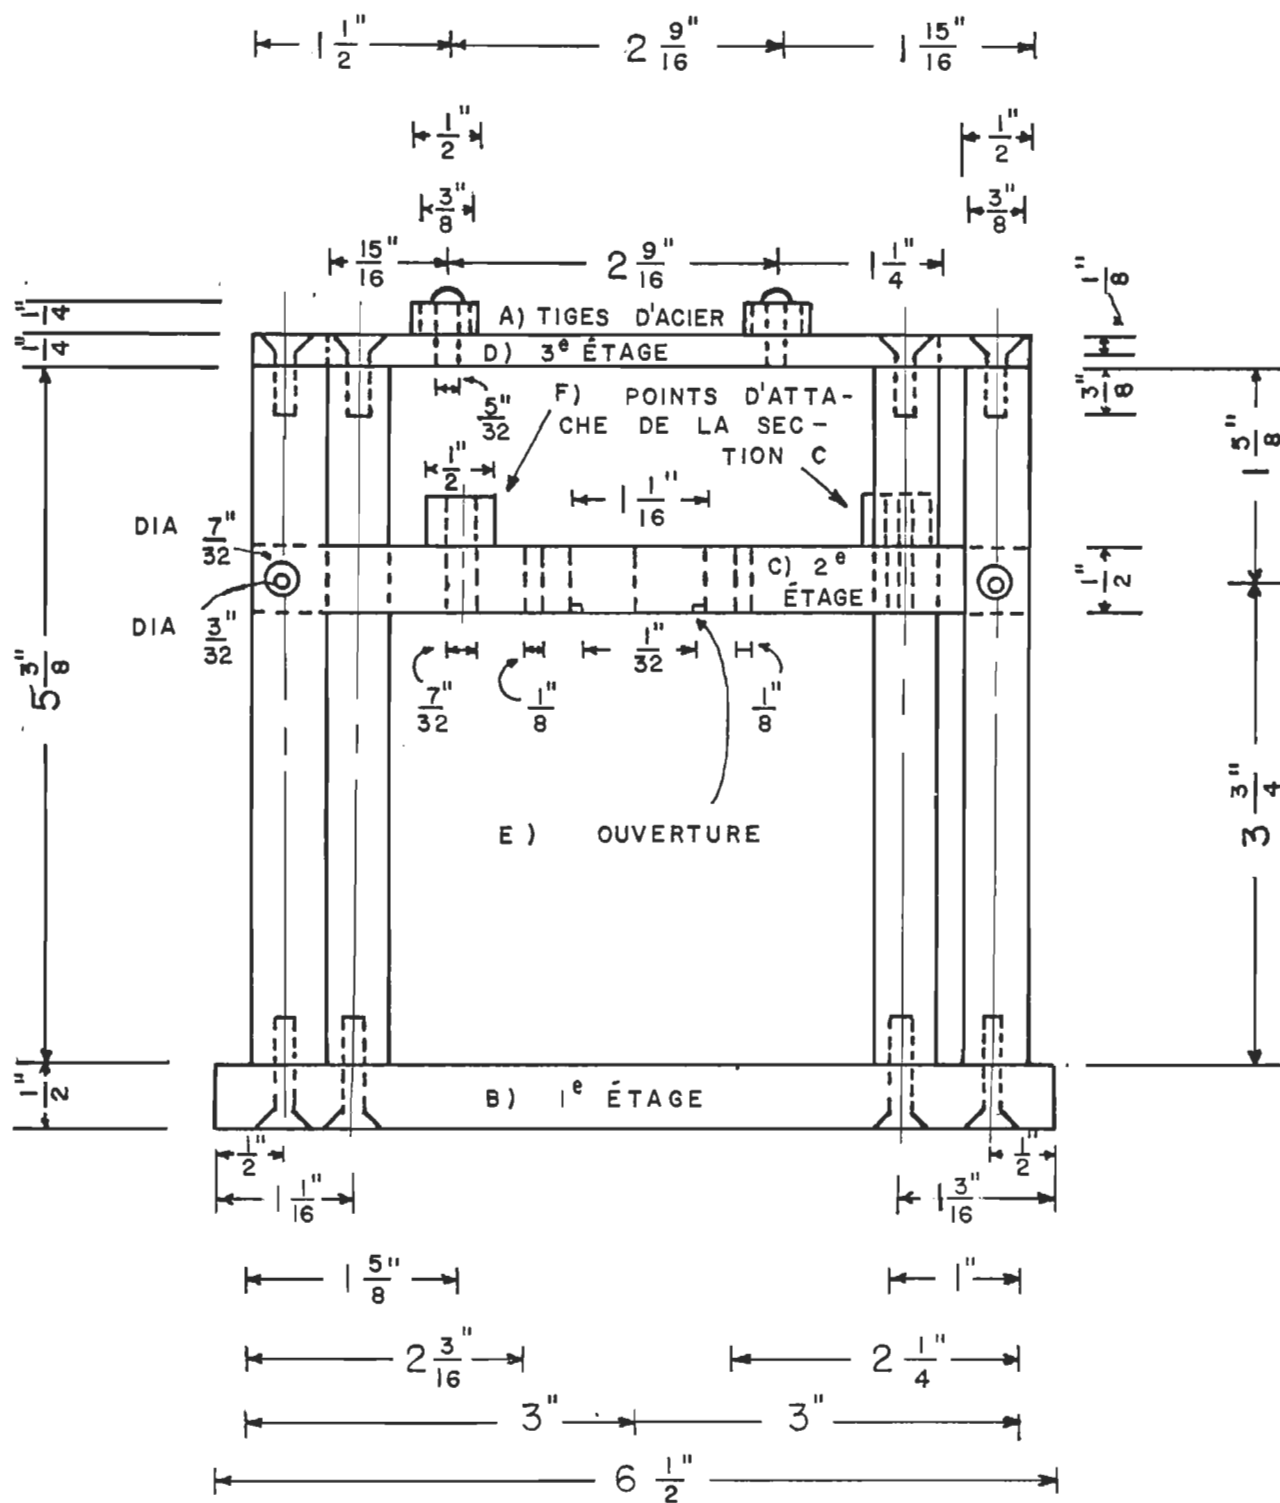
Plan détaillé de la section d vue dans le plan vertical nous faisant face.
